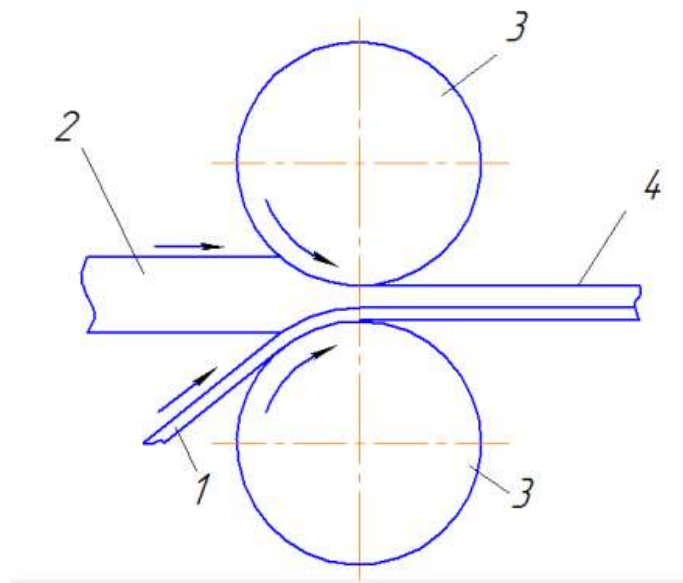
Получение биметаллов при деформации составляющей биметаллической композиции: 1 - твердая; 2 – мягкая; 3 – прокатные валки; 4 – биметалл.
